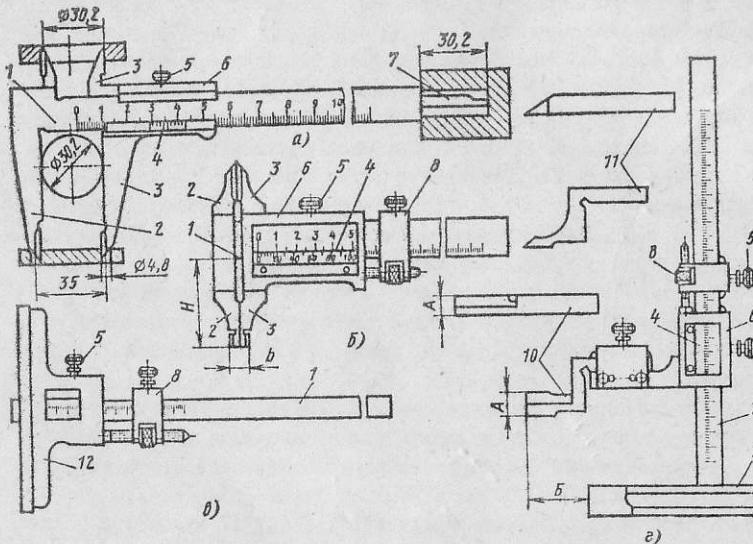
Рис. I. Штангенинструменты: а - штангенициркуль типа ШЦ-I;
